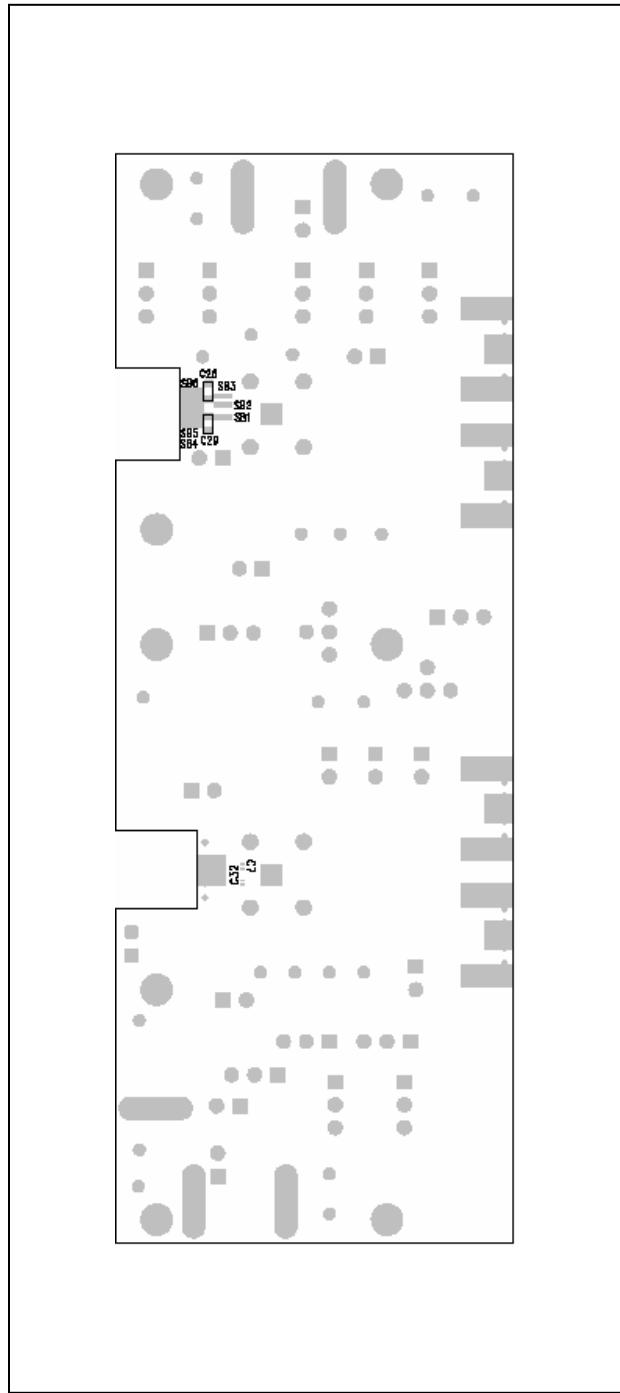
MAX3738 评估板 PCB 布局—焊接层
